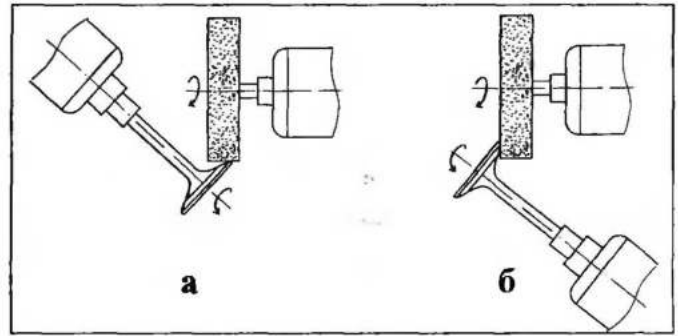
Схемы шлифования фаски клапана: а — наружной поверхностью шлифовального круга; б — боковой поверхностью шлифовального круга
